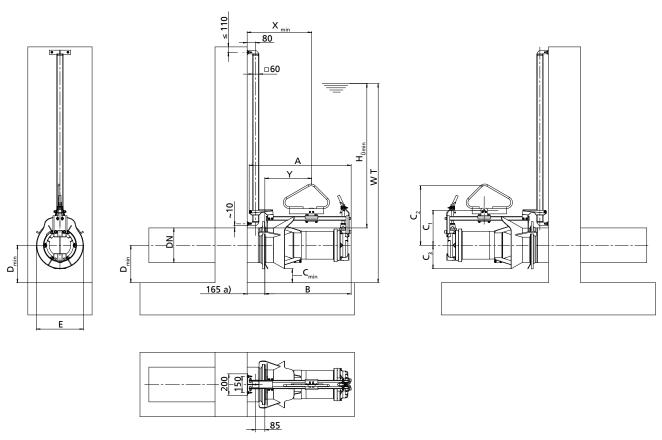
Dimensiones de Amaline 200, 300, 400 - material de la carcasa del motor: acero inoxidable
